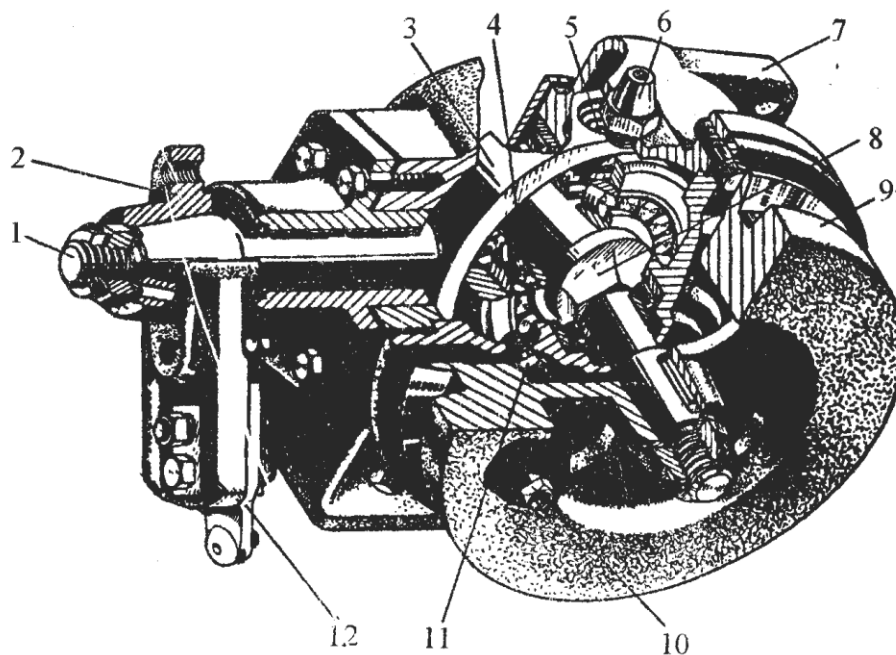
Механизм качающейся шайбы: 1 – входной вал; 2 – рычаг; 3 – водило; 4 – подшипник; 5 – палец; 6 – сапун; 7 – корпус; 8 – ведущий вал; 9 – шкив-маховик; 10 – пробка сливного отверстия; 11 – пробка отверстия для контроля уровня масла; 12 – головка
